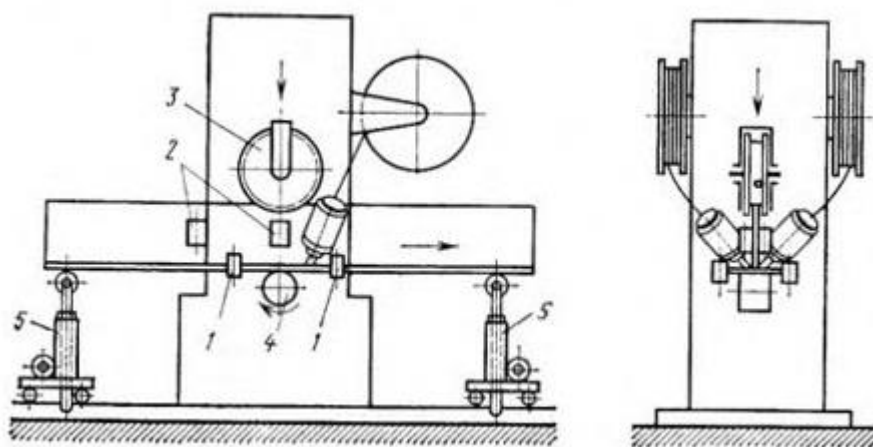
Схема станка СТС для сварки балок таврового профиля
